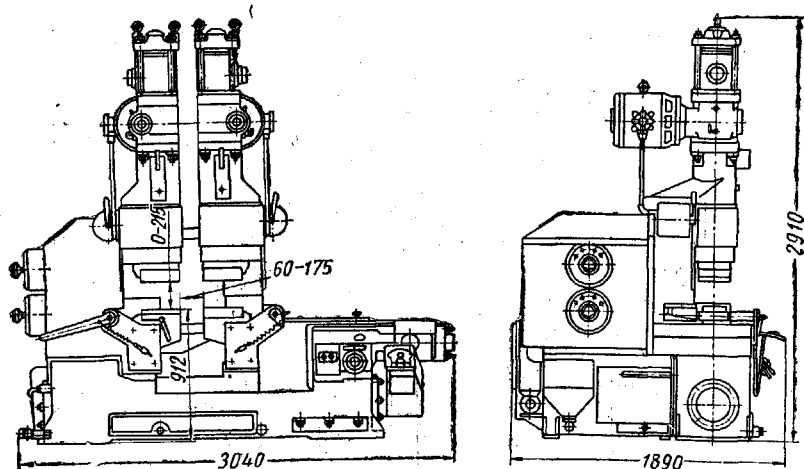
Автоматическая стыковая машина MSM-150-3 для сварки непрерывным оплавлением
